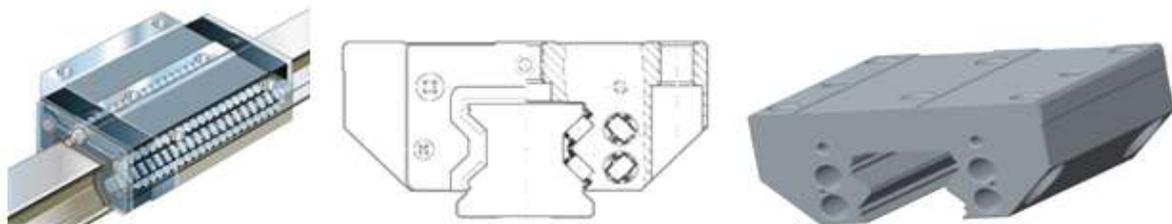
Rollenwagen mit Rücklaufbohrungen
